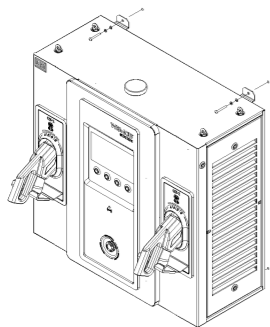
Ejemplo de fijación de la estación WEMOB-STATION (60/80 kW) a la estructura de concreto
